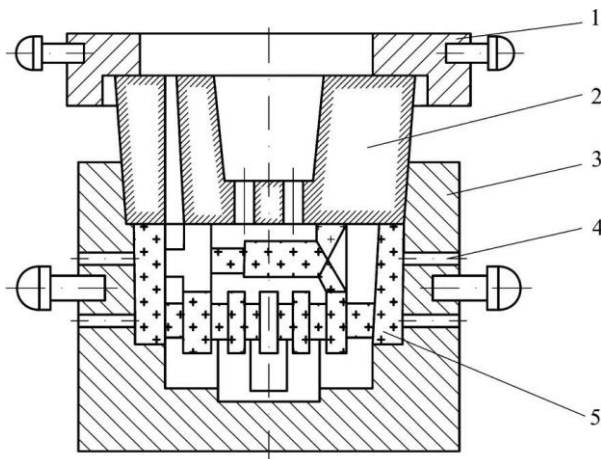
Вытряхной кокиль: 1 - груз; 2 - песчаная чаша; 3 - кокиль; 4 - вентиляционный канал; 5 - песчаный стержень
